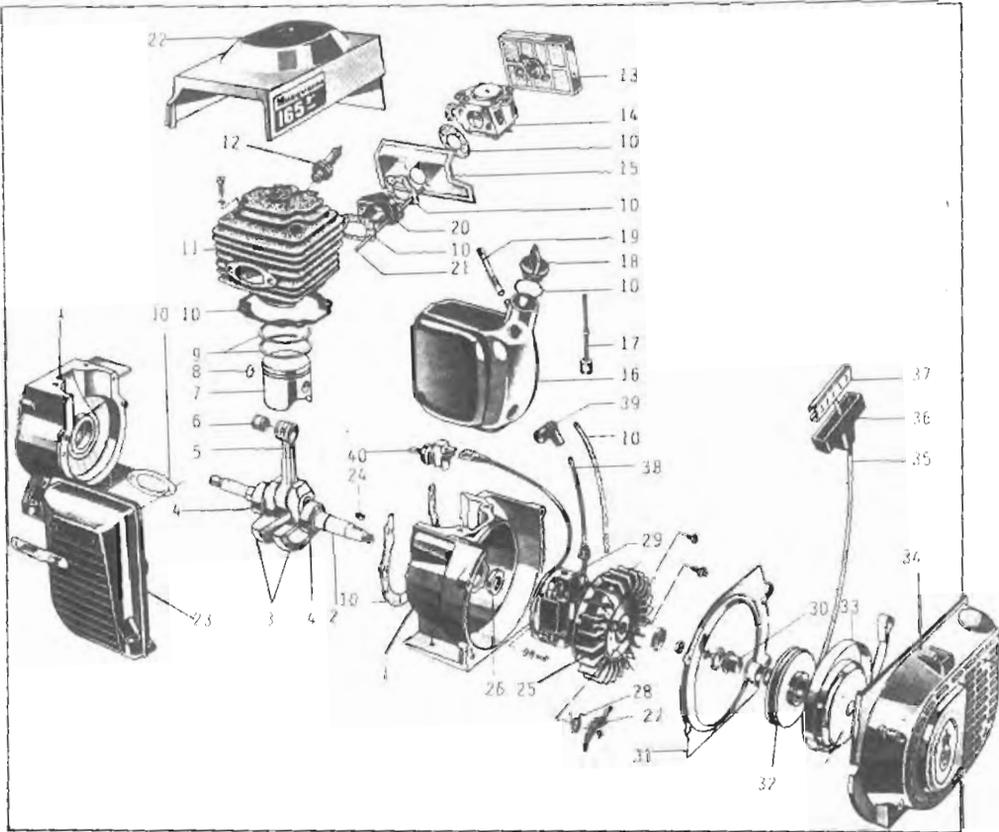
Despiece de un motor de dos tiempos (HUSQVARNA). 1.- Senicárteres. 2.- Cigüeñal. 3.- Contrapesos del cigüeñal. 4.- Rodamientos de bolas. 5.- Biela. 6.- Rodamiento de agujas. 7.- Pistón. 8.- Frenillo o clip del bulón. 9.- Segnetos. 10.- Juntas. 11.- Conjunto bloque-culata, provisto de aletas de refrigeración. 12.- Bujía. 13.- Filtro de aire. 14.- Carburador de membrana. 15.- Caja del filtro. 16.- Depósito de combustible. 17.- Tubería flexible, provista de filtro y contrapeso, para aspirar combustible en cualquier posición. 18.- Tapón de llenado. 19.- Tubería de combustible que une el depósito con el carburador. 20.- Colector. 21.- Tornillo. 22.- Carcasa envolvente del cilindro. 23.- Silenciador. 24.- Chaveta. 25.- Volante provisto de aletas para la refrigeración. 26.- Retén. 27.- Patillas de conexión del sistema de arranque. 28.- Muelle. 29.- Sistema de encendido. 30.- Casquillo. 31.- Tapa interior del sistema de arranque. 32.- Polea. 33.- Fleje del sistema de arranque. 34.- Carcasa del sistema de arranque. 35.- Cuerda. 36.- Enpuñadura. 37.- Regleta. 38.- Cable de la bujía. 39.- Capuchón de la bujía. 40.- Interruptor de pare.
